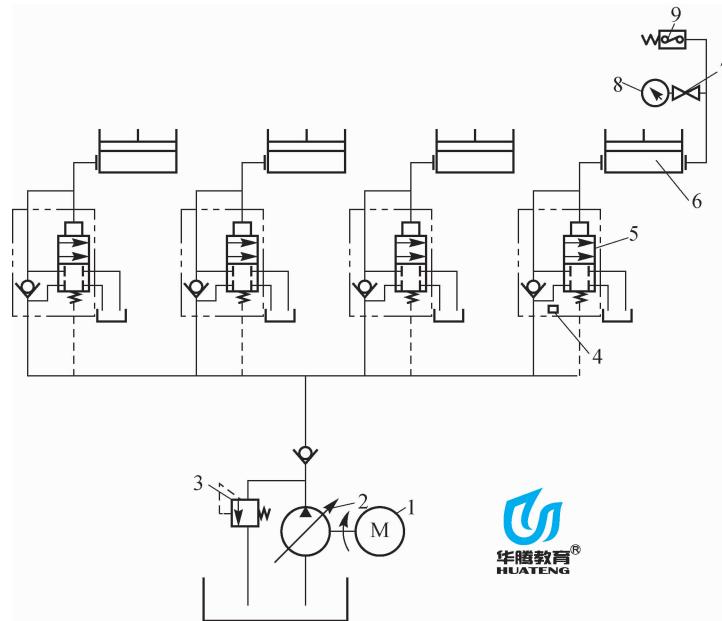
J39-800 型闭式四点压力机液压式过载保护装置工作原理图
